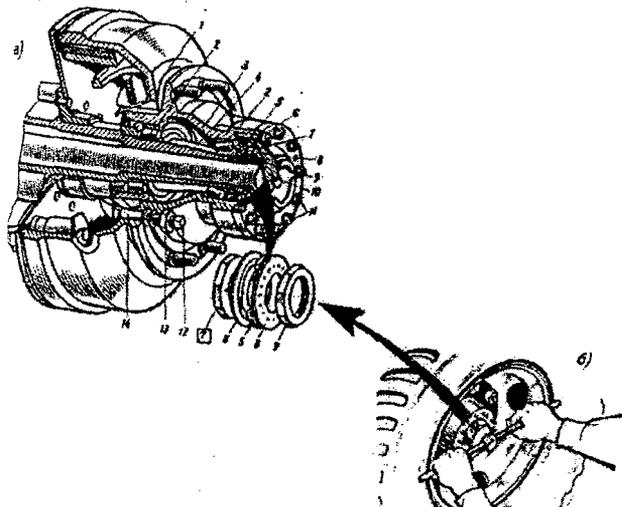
Регулировка подшипников ступиц грузовых автомобилей:
